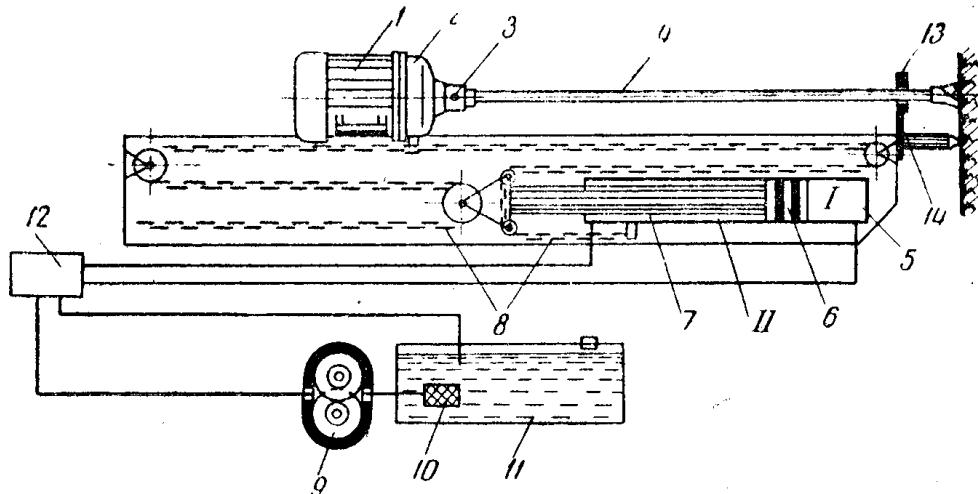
Кинематическая схема длинноходового сверла ЭБВ-1:
